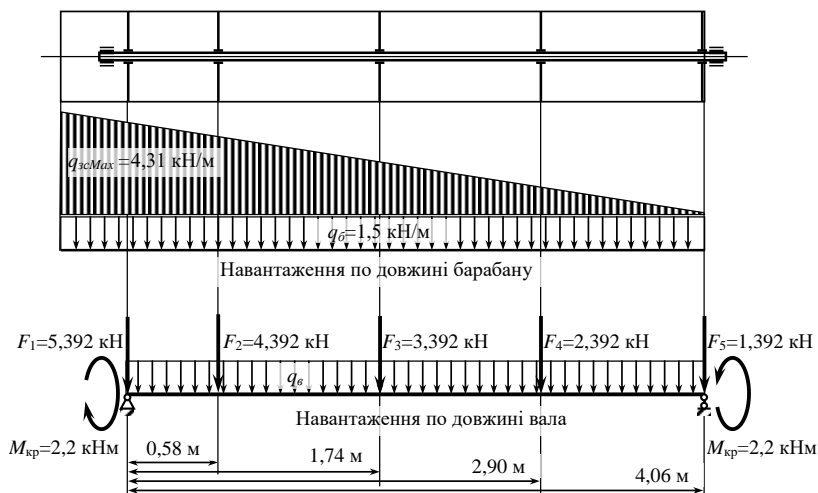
Формування розрахункової схеми навантаження вала сепаратора
